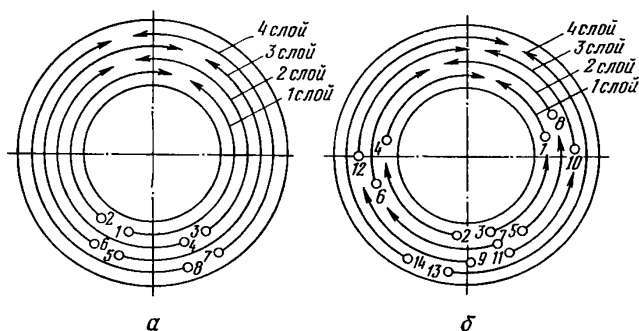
Порядок наложения слоев при сварке неповоротного стыка труб одним сварщиком:
